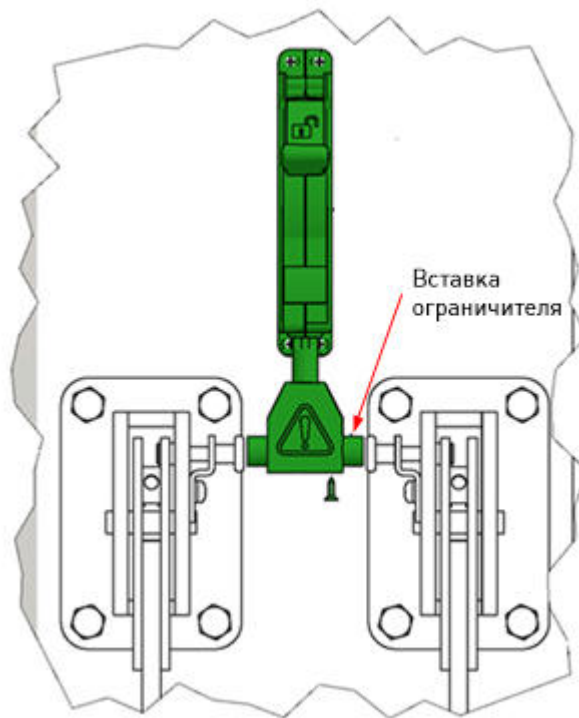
Установка блокиратора с разнесенными разъединителями
